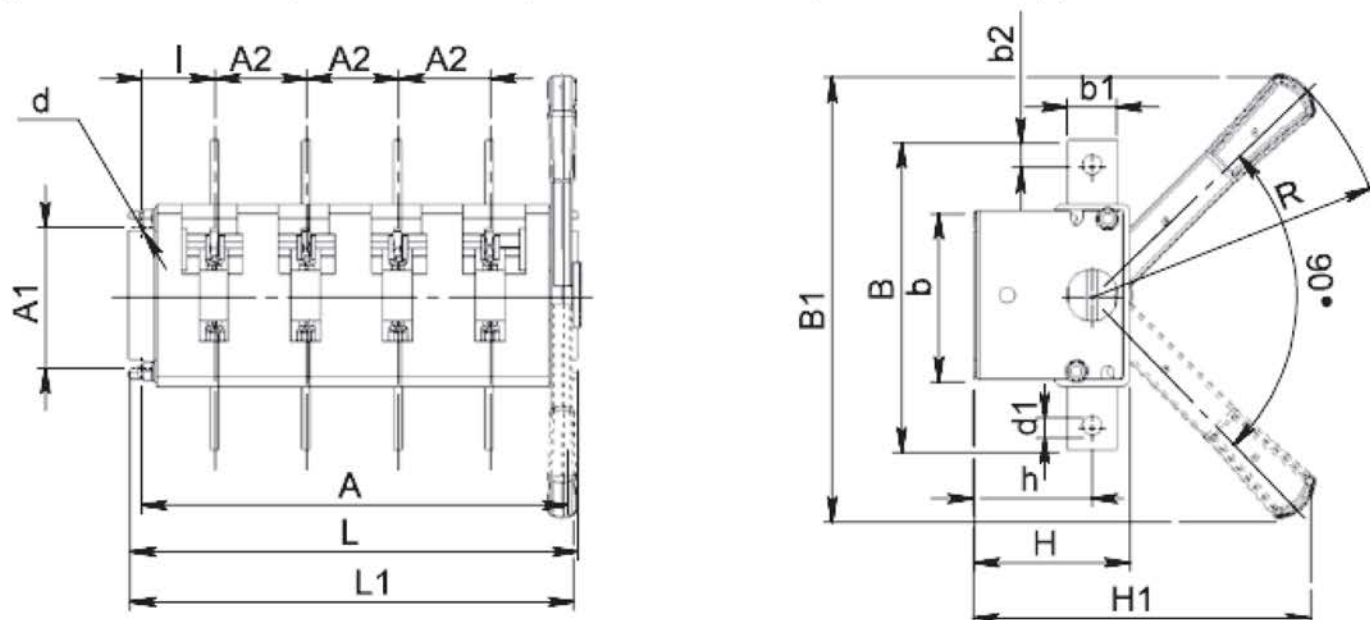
Выключатель-разъединитель четырехполюсный на одно направление с боковой смещенной рукояткой.
